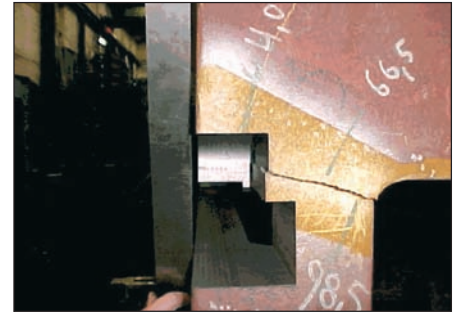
Bei der Bearbeitung gerissener Maschinentisch aus EN-GJS-400-15, der erfolgreich wieder geschweißt werden konnte.
